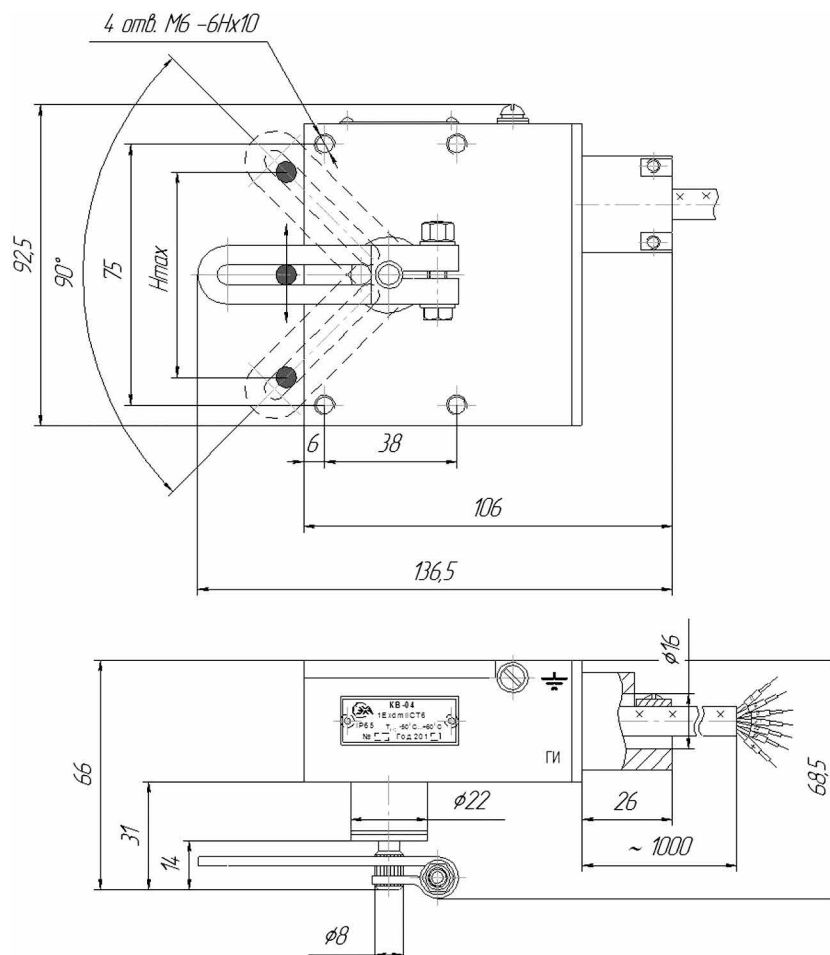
Габаритные и установочные размеры выключателя КВ-04
